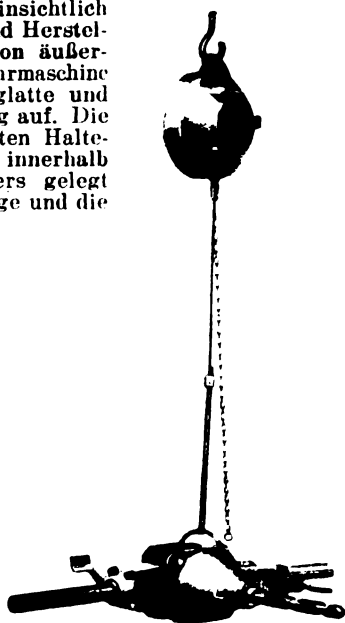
Aufhängung einer Handbohrmaschine für gewichtlose Arbeiten.
